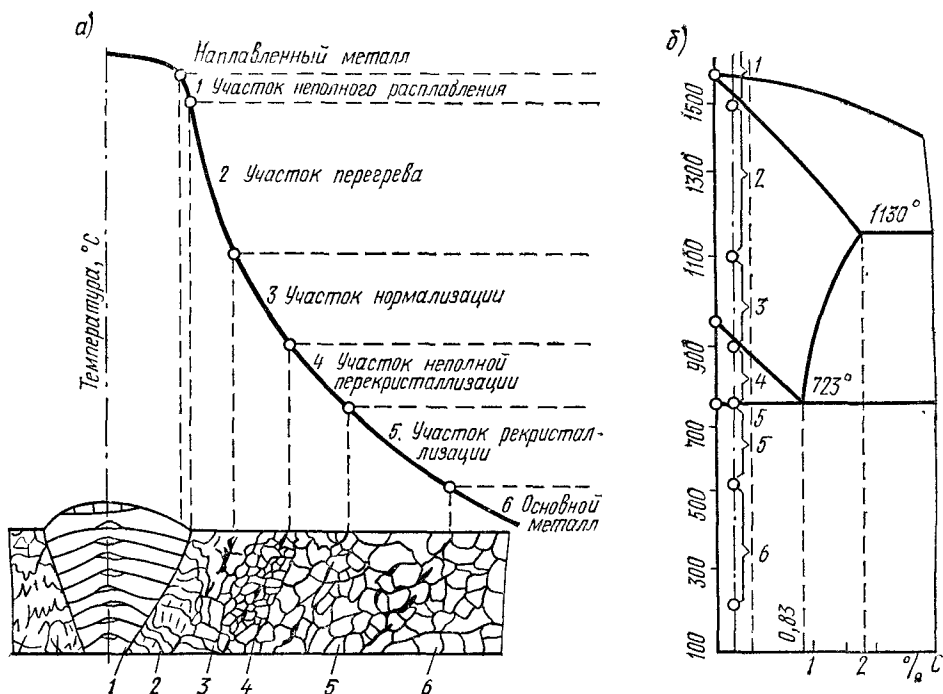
Зона термического влияния сварного шва малоуглеродистой стали
